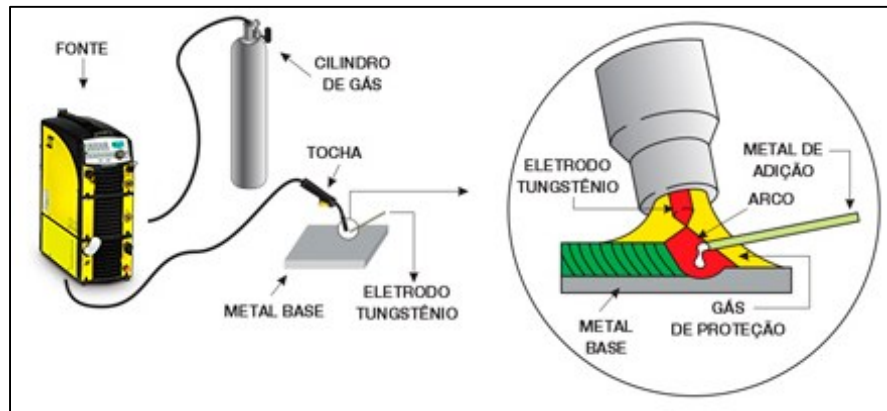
Processo de Soldagem TIG Fonte: ESAB
